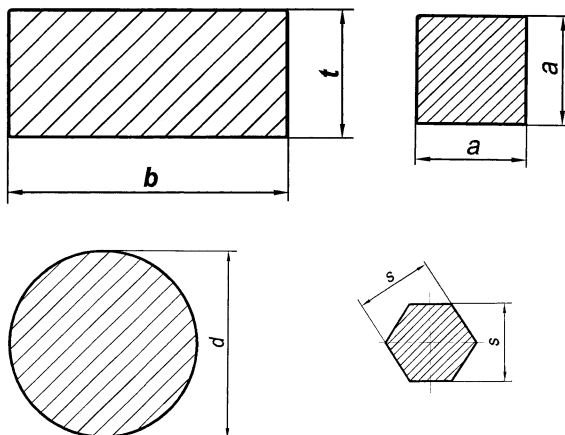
DIN EN 10058 warmgewalzter Flachstahl, DIN EN 10059 warmgewalzter Vierkantstab, DIN EN 10060 warmgewalzter Rundstab, DIN EN 10061 warmgewalzter Sechskantstab
